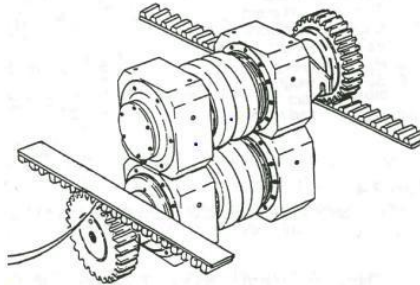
Візуалізація приводу ведуча шестерня – нерухома зубчаста рейка на сучасних станах холодної пільгерної прокатки [2]
